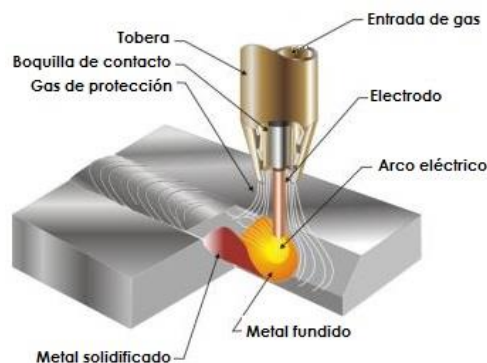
Elementos Principales Soldadura MIG-MAG
